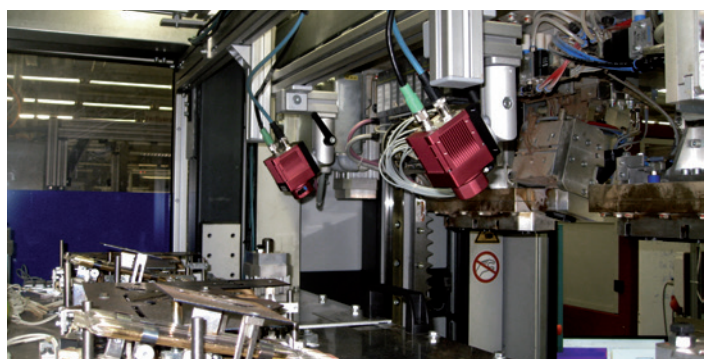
In eine Schweißanlage integrierte Infrarotkameras
